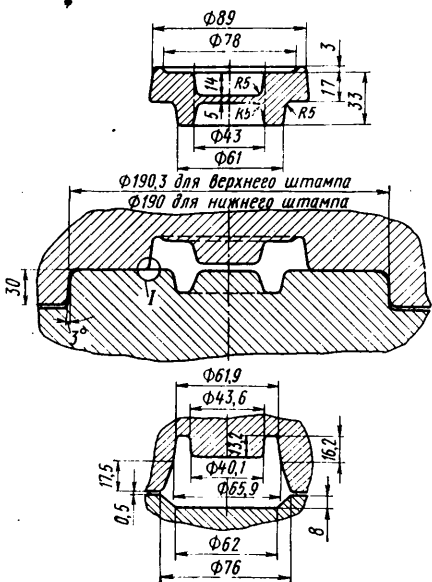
Поковка и конструкция молотового штампа (второй вариант). В нижней части чертежа показан специальный высадочный ручей молотового штампа
